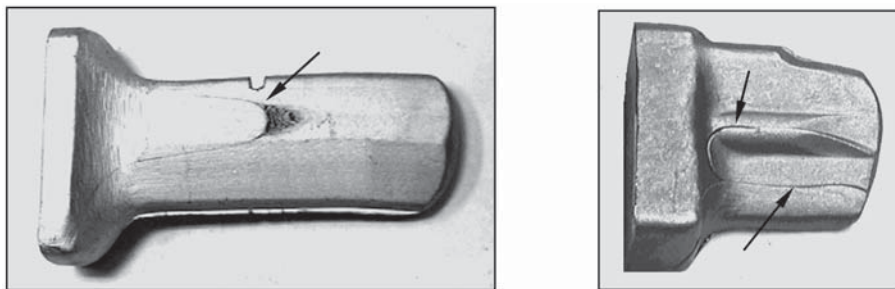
Производственный дефект в виде расслоения металла при выдавливании промежуточной заготовки лопатки газотурбинного двигателя
